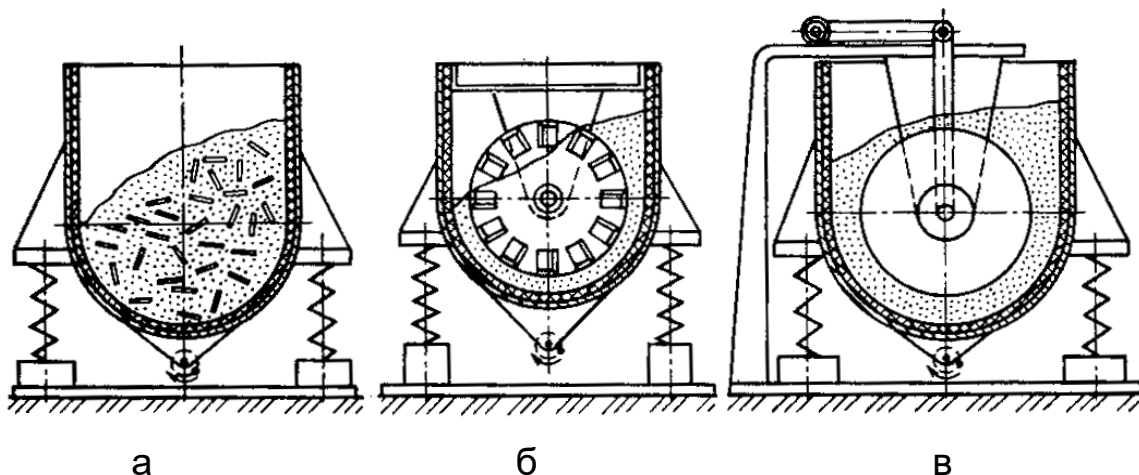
Способы загрузки деталей при виброупрочнении:
